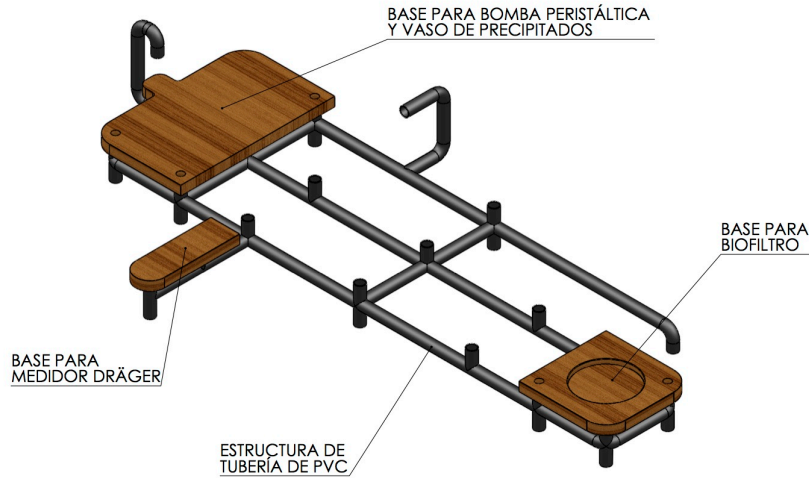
Modelo que muestra las bases utilizadas para los equipos del sistema. Para mayor detalle, ver Anexo: Planos.
